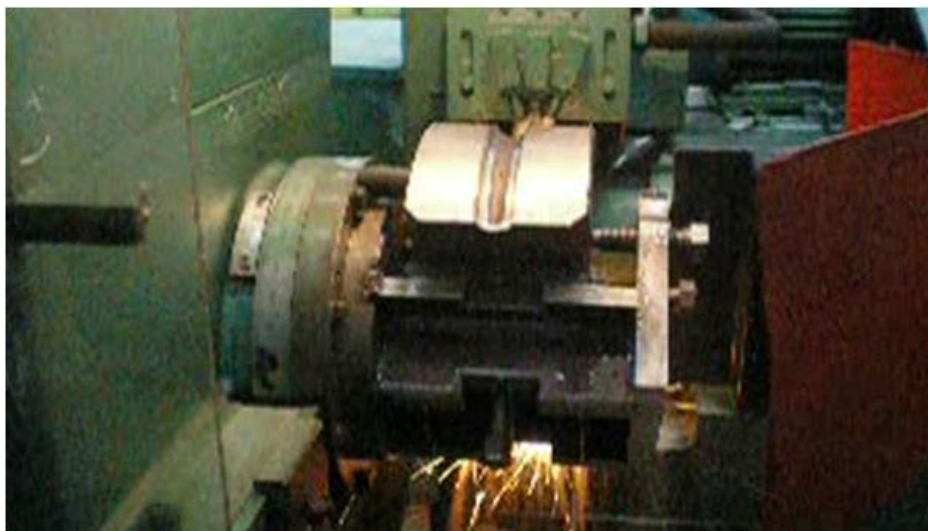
фінішна абразивна обробка робочої поверхні калібру.
